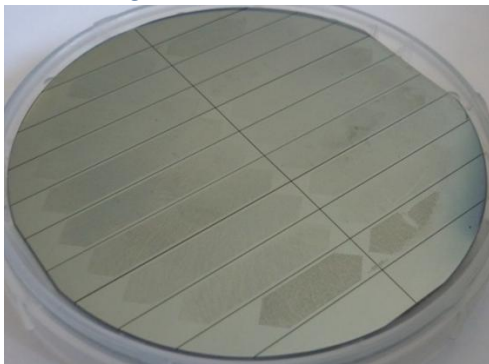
Géométries des motifs de soudure en BCB pour la réalisation des éprouvettes
